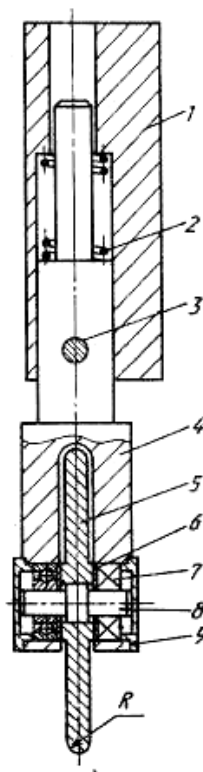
Одно роликовий обкатувальний пристрій.
